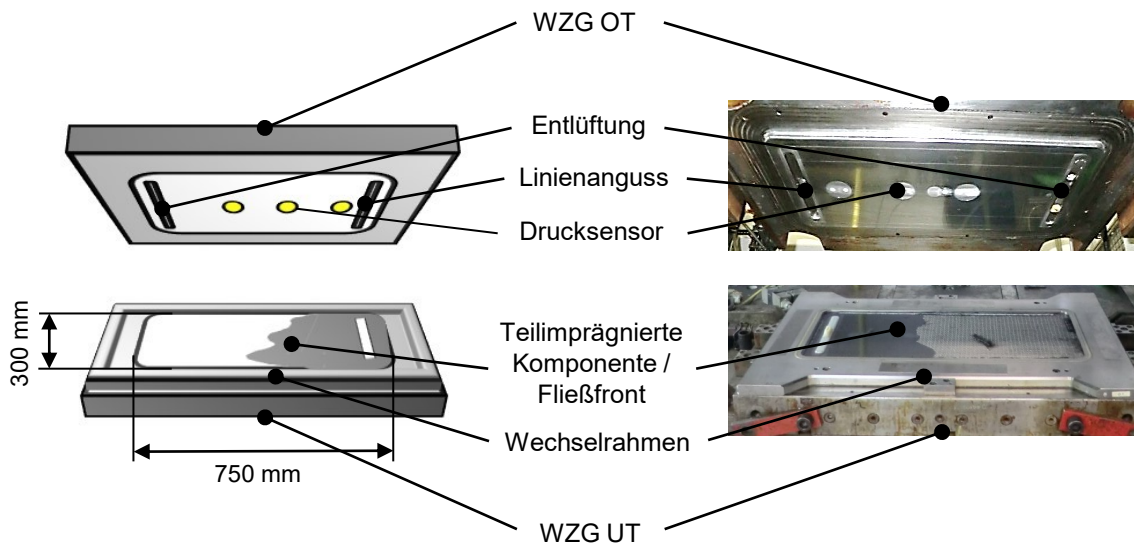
Werkzeugober- und -unterteil des Plattenwerkzeugs.
